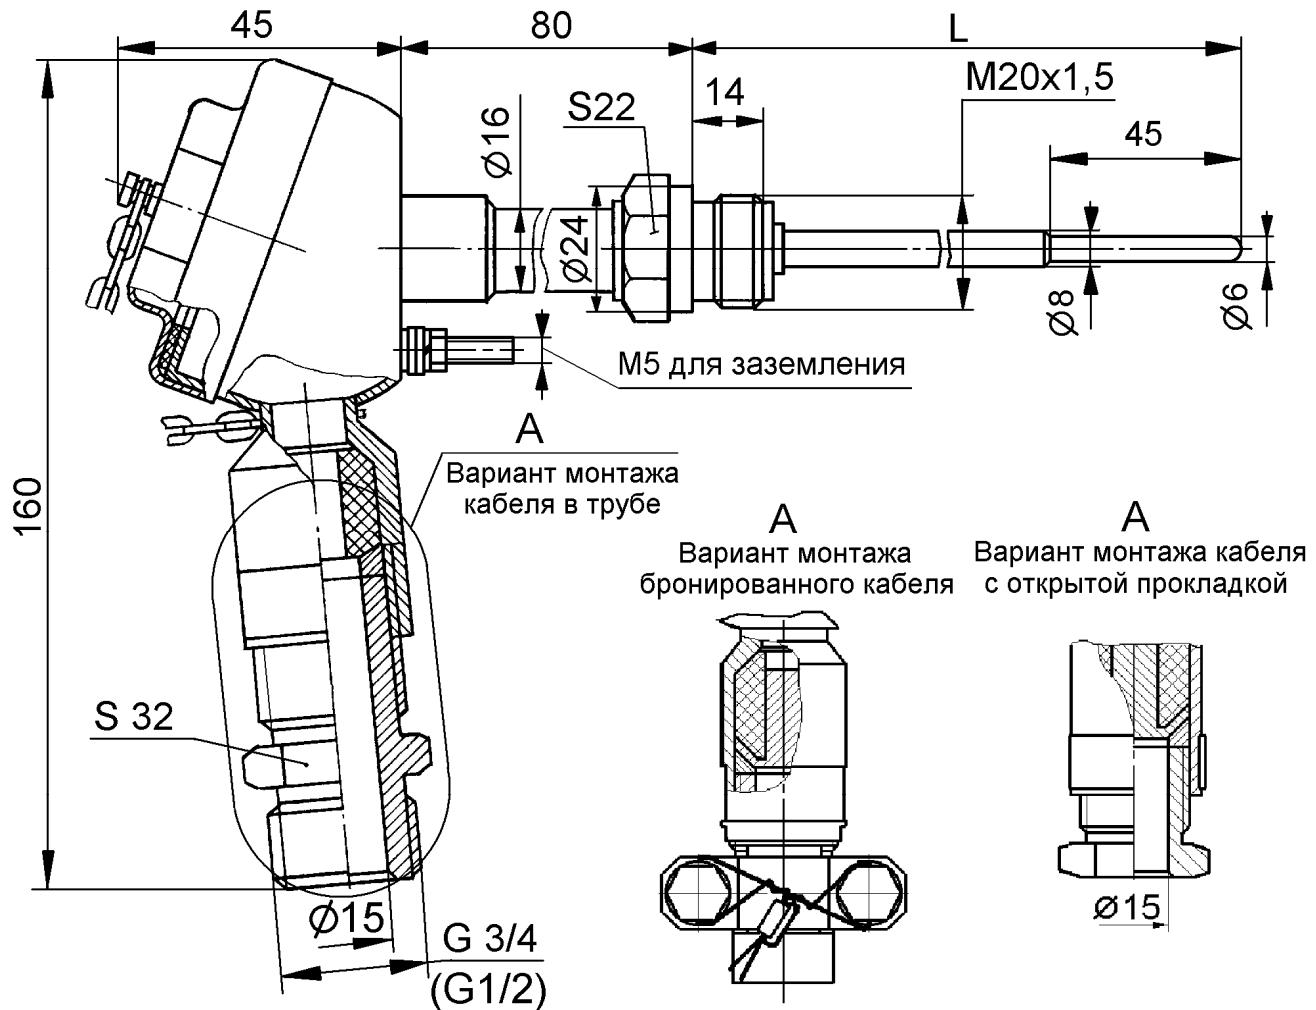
Штуцер неподвижный, головка из нержавеющей стали
